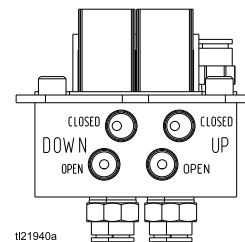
Schlauchanschlüsse am Magnetventilverteiler, zum Pumpenauslassverteiler
